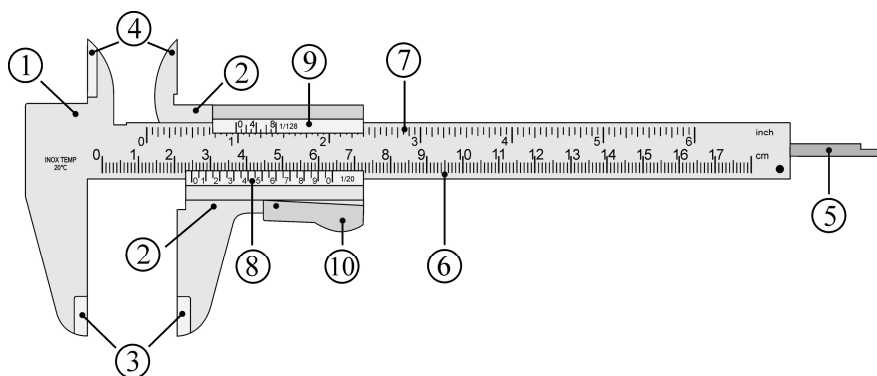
Будова штангенциркуля: 1 – штанга; 2 – рухома рамка; 3 – зовнішні губки для вимірювання зовнішніх розмірів; 4 – внутрішні губки для вимірювання внутрішніх розмірів; 5 – щуп для вимірювання глибини; 6 – основна шкала, см; 7 – основна шкала, дюймів; 8 – ноніус для визначення десятих частин міліметра; 9 – ноніус для визначення частин дюйма; 10 – фіксатор рухої частини приладу для полегшення процедури вимірювання
